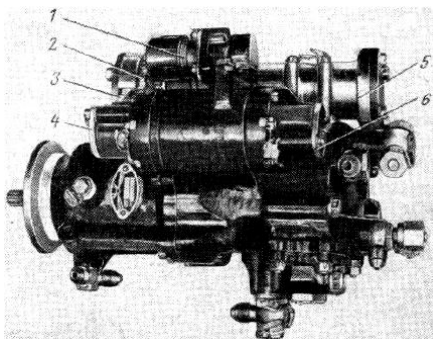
Командный агрегат КА-40 (внешний вид с правой стороны):
